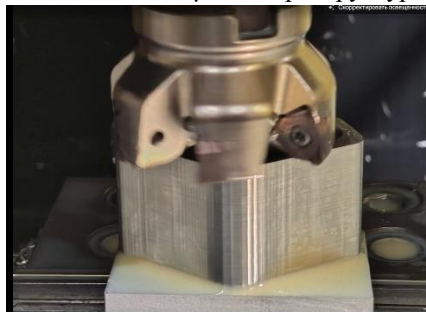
Обробка заготовки за допомогою багатолезового інструмента зі змінними пластинами
